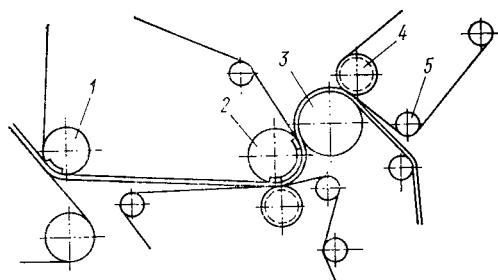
Схема прессовой части с закрытой проводкой полотна
